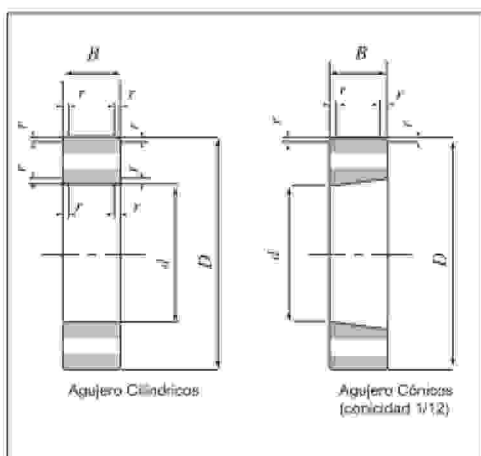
Dimensiones Principales de los Rodamientos Radiales (Excepto Rodamientos de Rodillos Cónicos).
